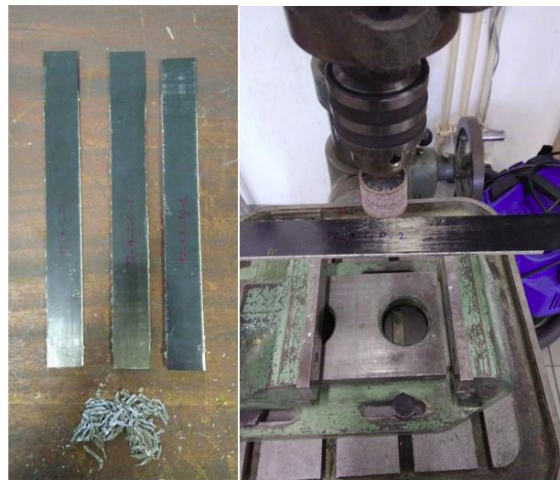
Excessos a serem removidos das extremidades do provete [81].
